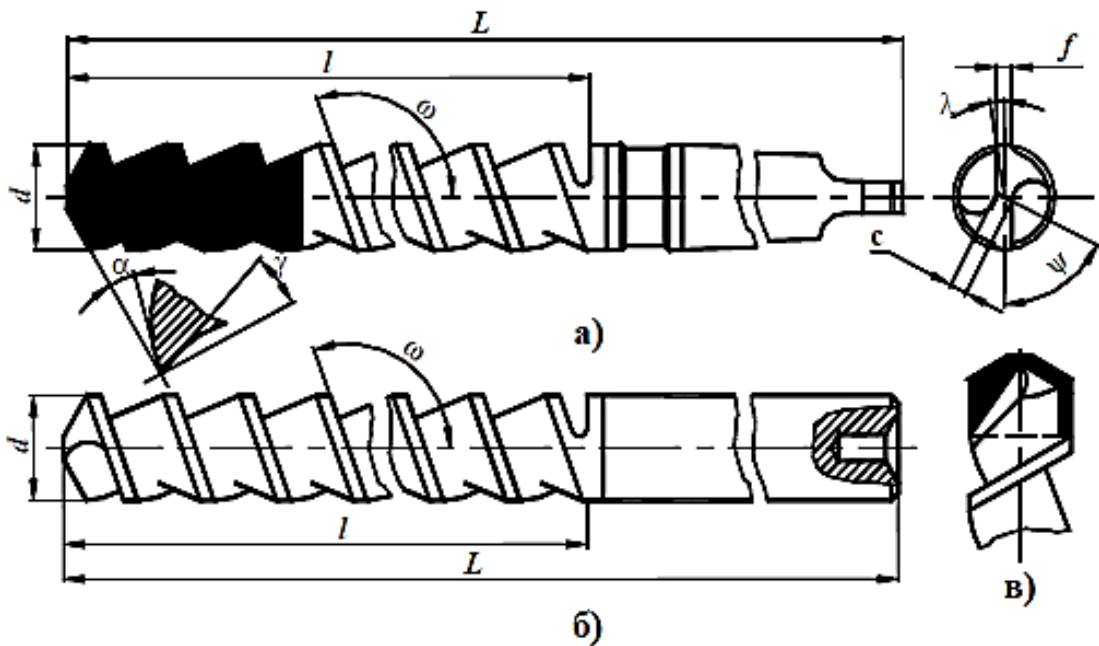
Геометричні параметри і конструктивні елементи шнекового свердла. а) зварне з конічним хвостовиком; б) цільне з циліндричним хвостовиком; в) з напаяною твердосплавною пластинкою. d - діаметр; L - довжина; l - довжина робочої частини; α - задній кут; γ - передній кут; λ - кут нахилу ГРК; ψ - кут нахилу перемички; f - ширина допоміжної стрічки; ω - кут нахилу гвинтової канавки; c - довжина перемички (товщина серцевини інструменту).
